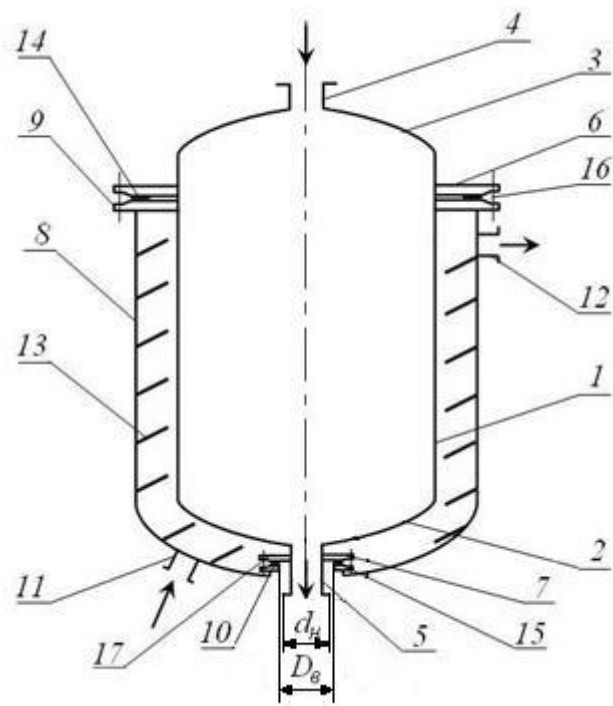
Общий вид реактора со съёмной U-образной рубашкой:
